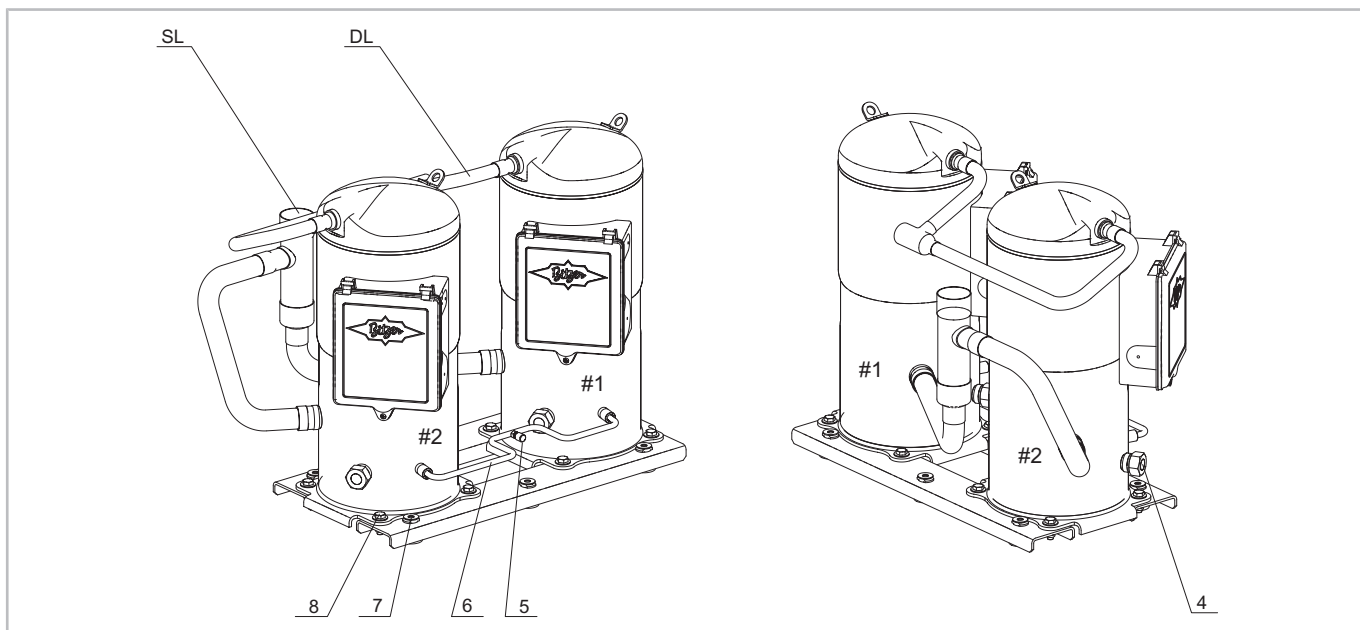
Пример равного или неравного тандем объединения компрессоров ORBIT 6 с BITZER Advanced Header Technology (вертикальный ВАНТ header)
